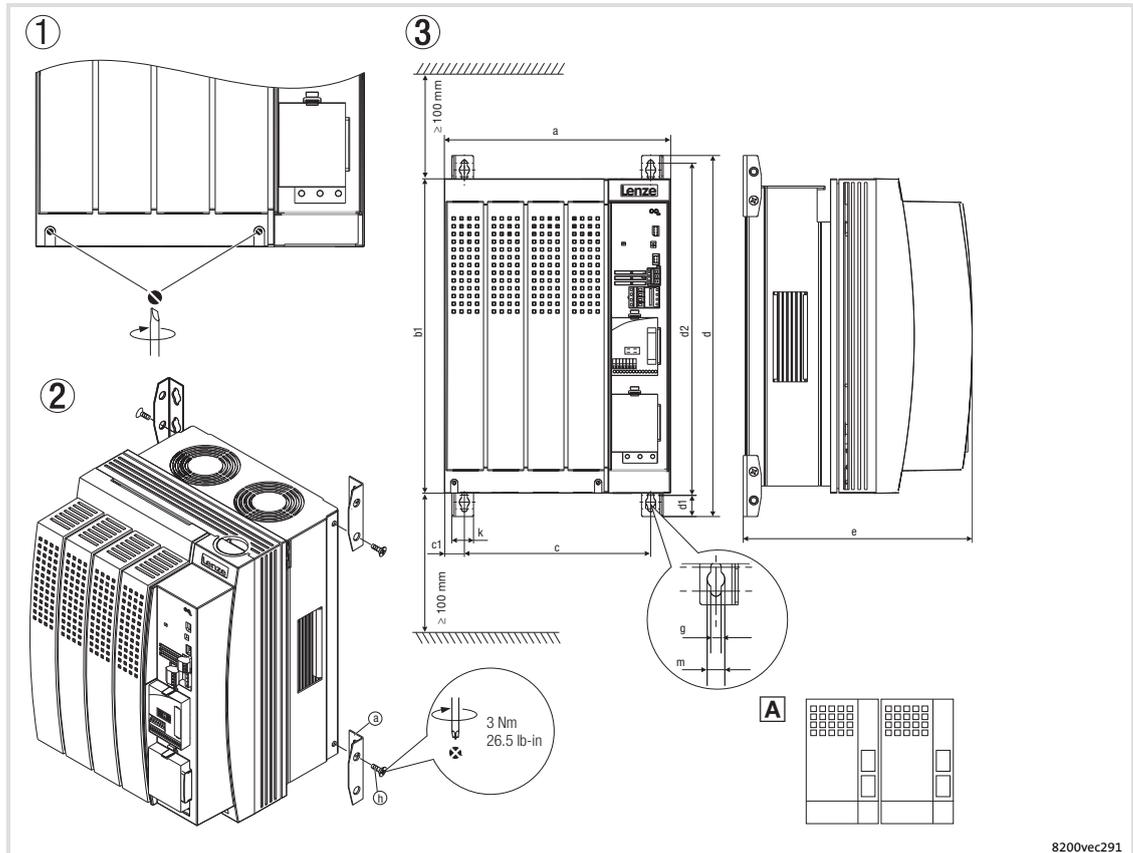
Standardmontage mit Befestigungswinkel 15 ... 30 kW
